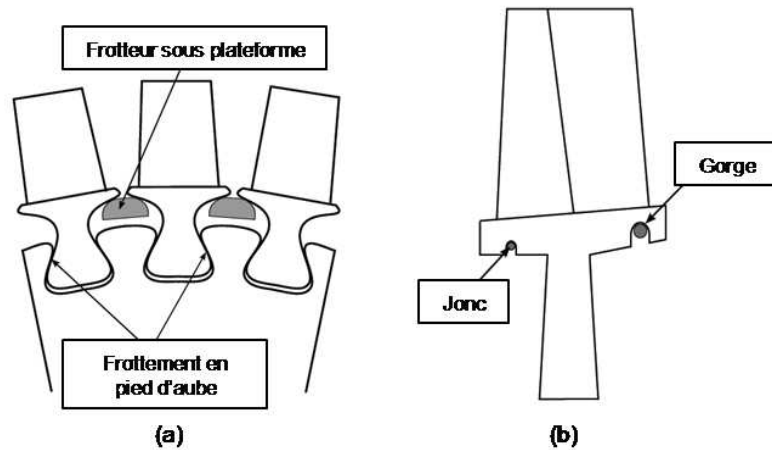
Assemblage aubes-disques munis de frotteurs sous plateforme (a) et implantations des joncs de friction sur un disque aubagé monobloc (b) [LAXALDE07c].
